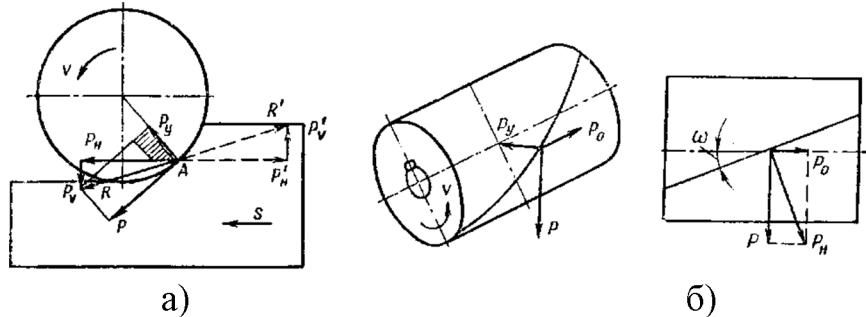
Силы резания при работе цилиндрической фрезой
